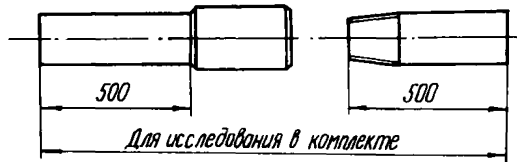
Разрушение резьбового соединения, разрушение или трещина муфты, повреждение резьбы
